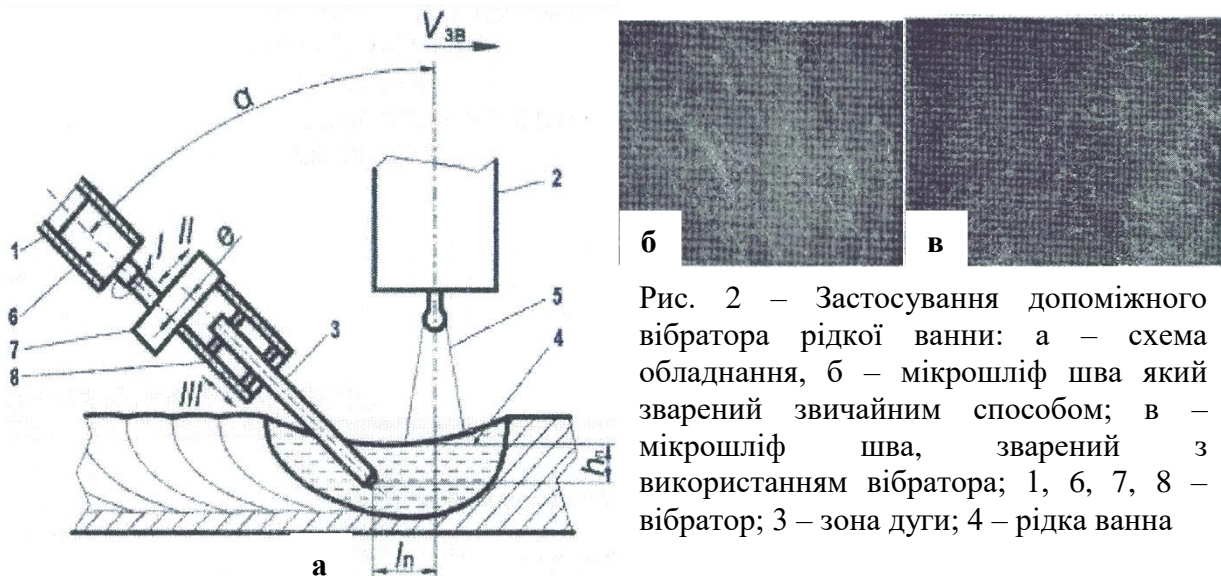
Застосування допоміжного вібратора рідкої ванни: а – схема обладнання, б – мікрошліф шва який зварений звичайним способом; в – мікрошліф шва, зварений з використанням вібратора; 1, 6, 7, 8 – вібратор; 3 – зона дуги; 4 – рідка ванна
